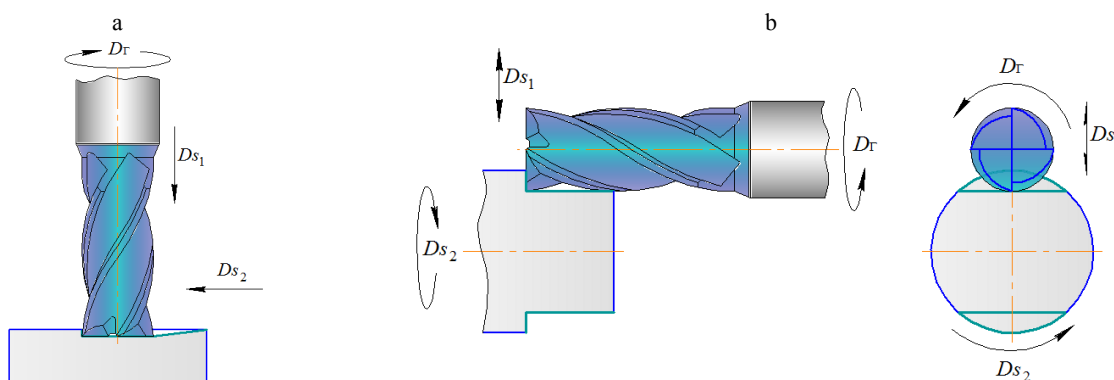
Схемы обработки с врезанием фрезы по касательной: а – плоской поверхности детали; б – плоской и цилиндрической поверхностях детали
